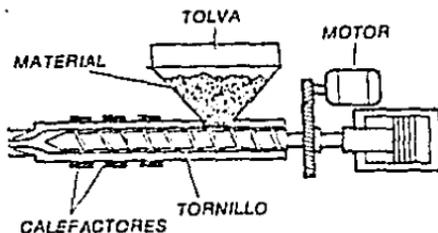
Unidad de inyección de una máquina de molde de materiales termoplásticos por inyección estilo tornillo.
